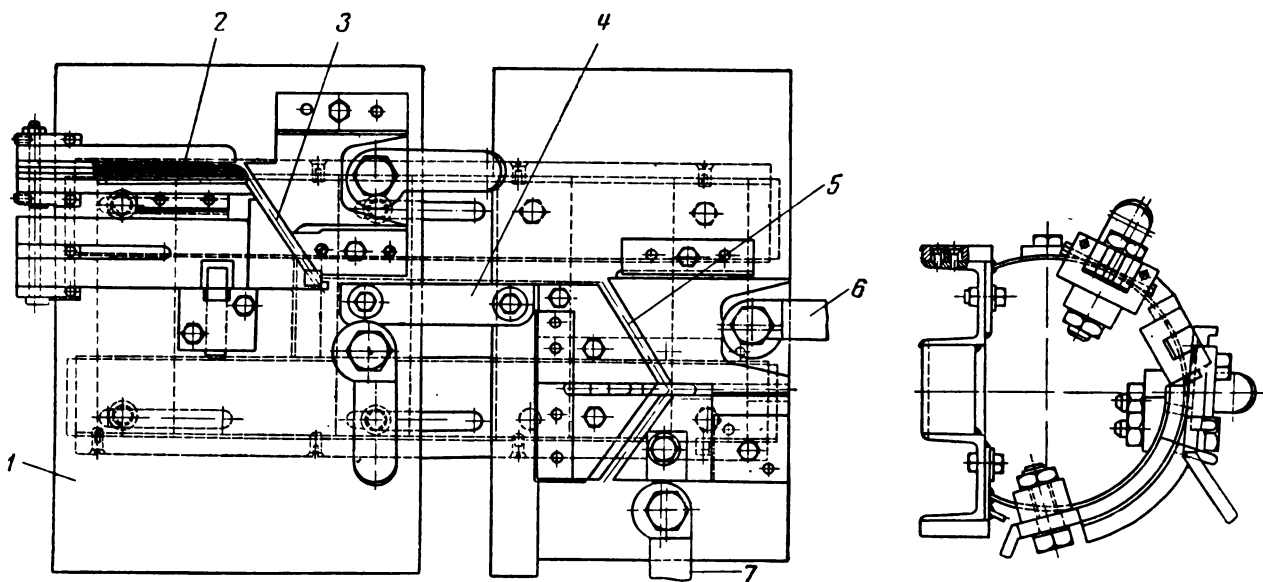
Приспособление для формовки одновитковых катушек.
